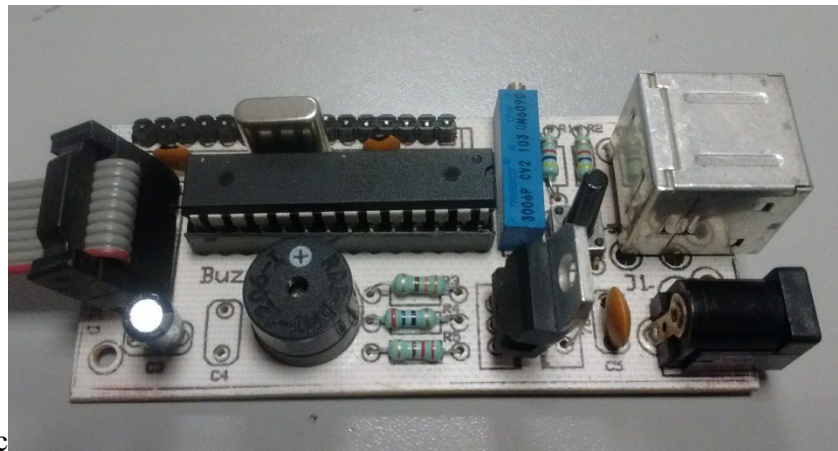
Tarjeta PCB con los componentes soldados en su primera versión
